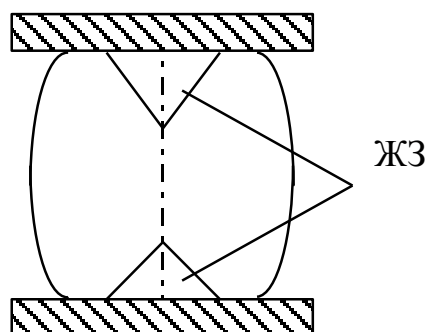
Схема осадки на шероховатых бойках: ЖЗ - жесткие зоны
